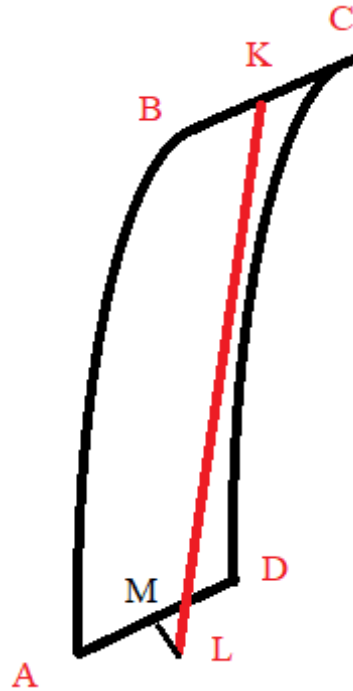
Схематичне зображення приводу пружного елемента пальця захвату [28].
